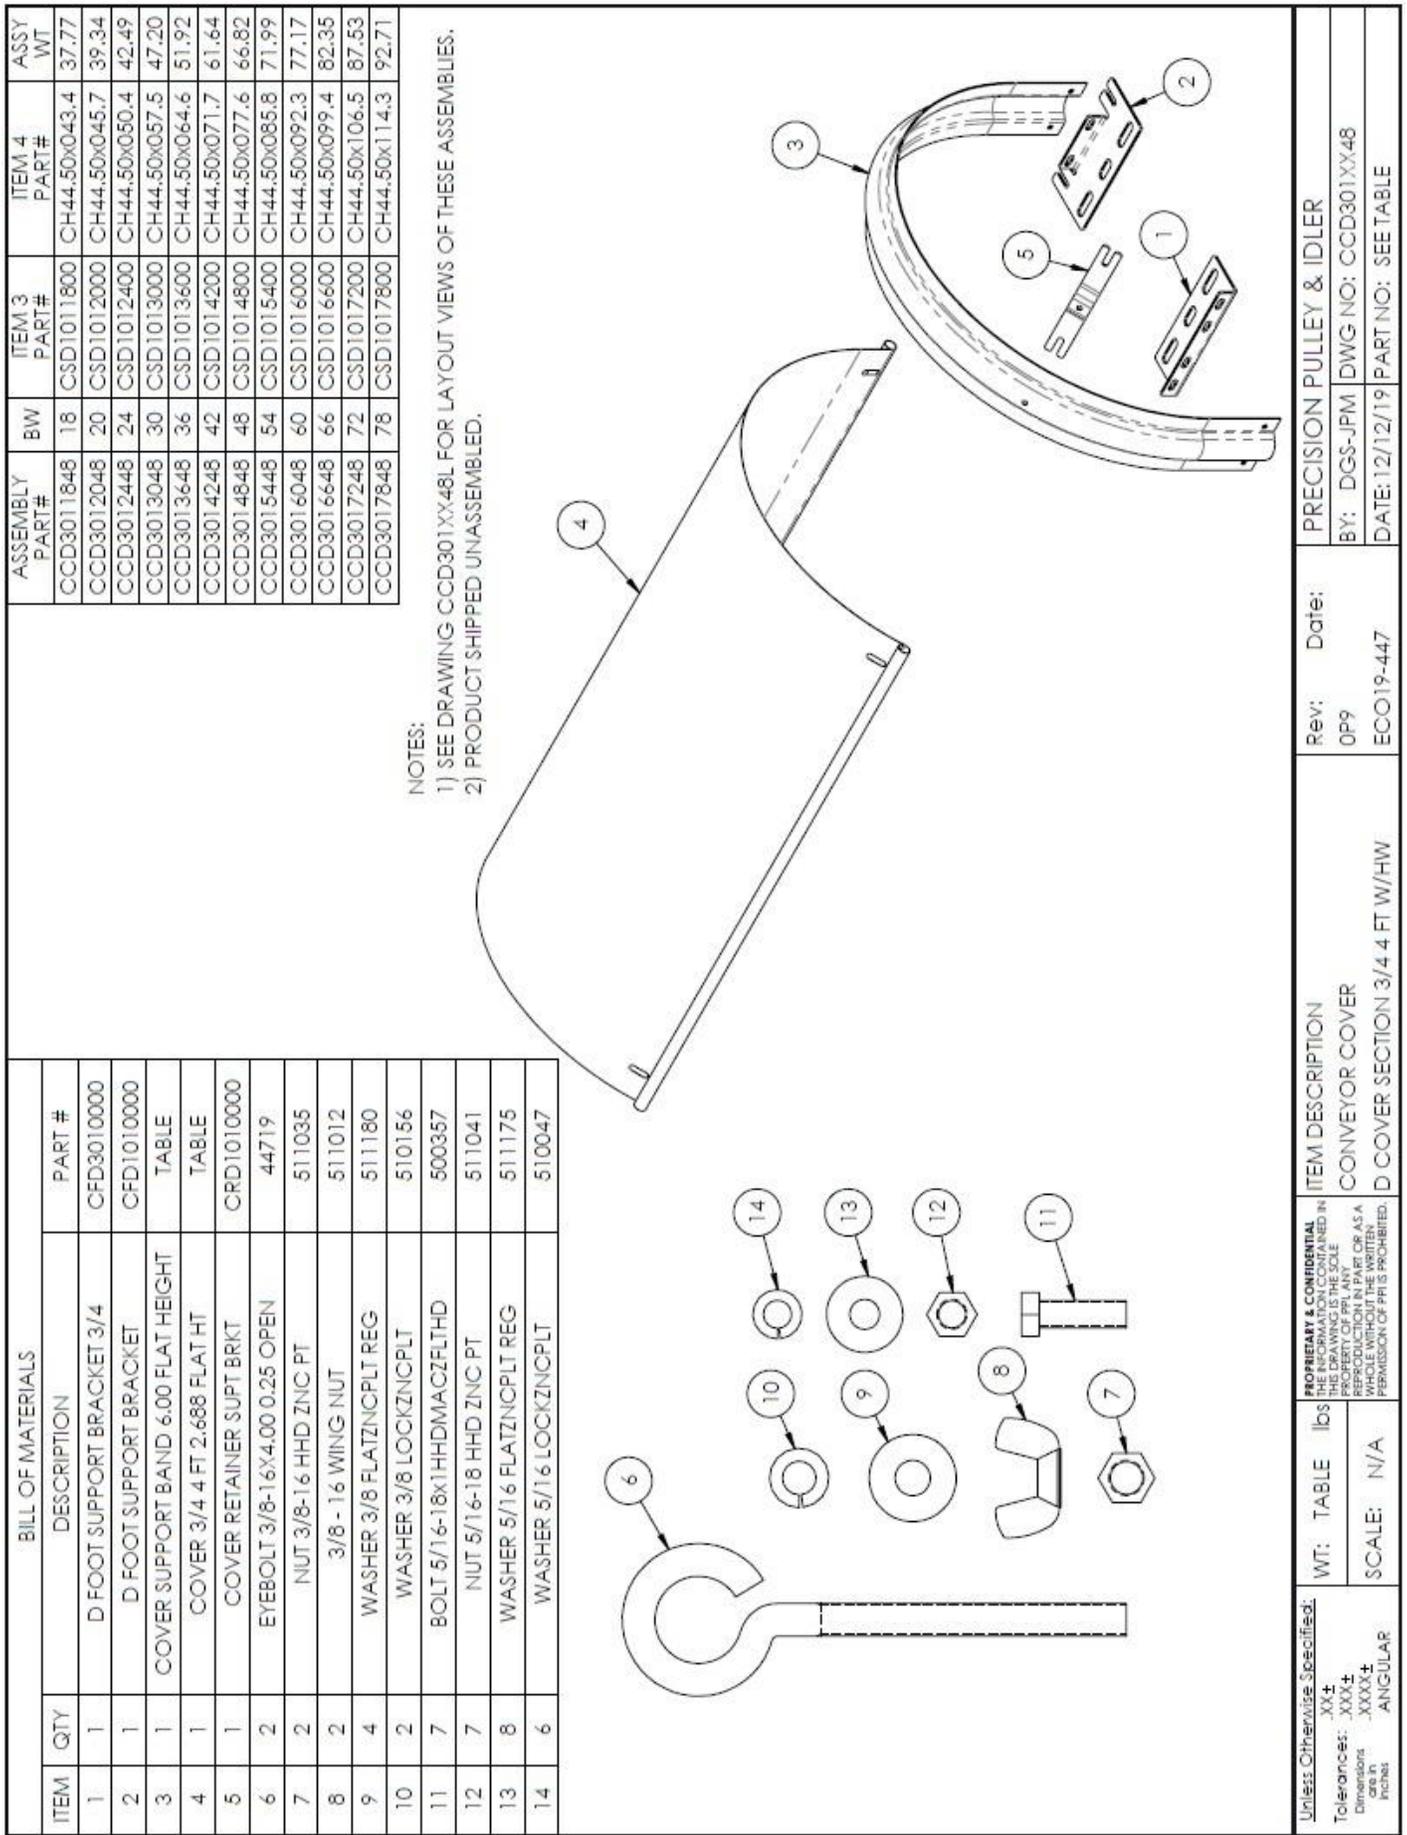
D, SECCIÓN CUBIERTA ¾, 4 PIES CON ELEMENTOS DE SUJECIÓN
